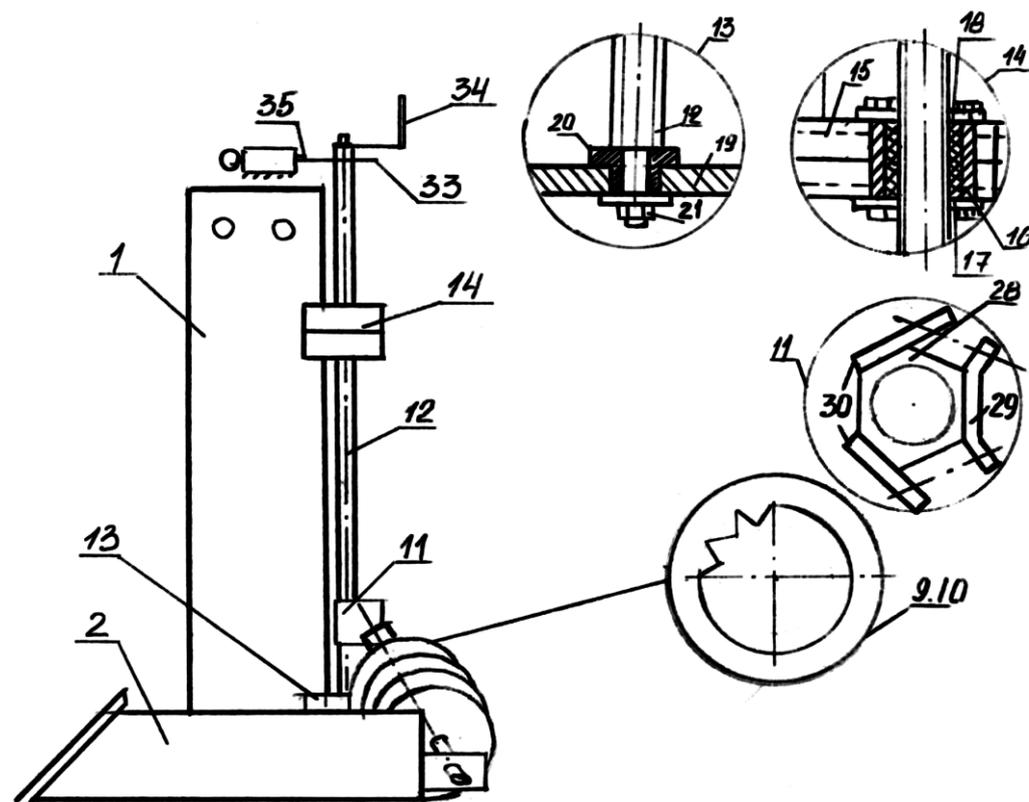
Почвообрабатывающий рабочий орган, вид сбоку
